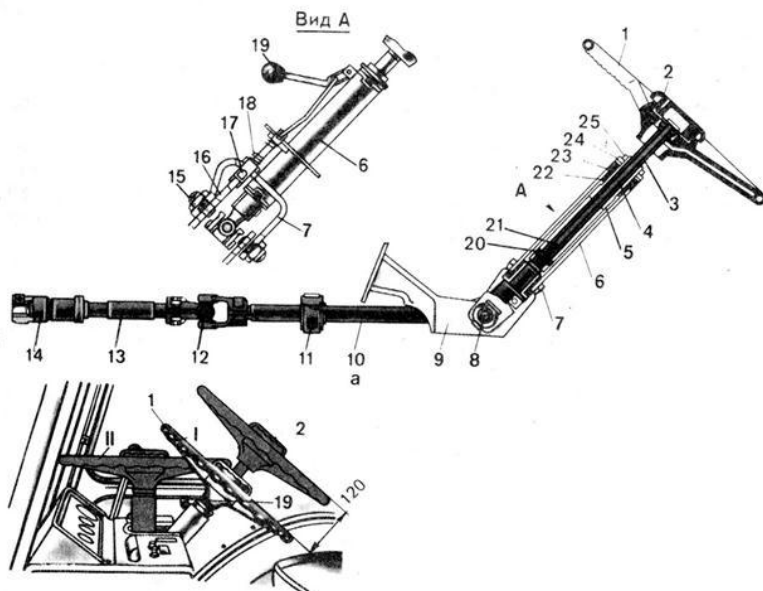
Привод рулевого механизма трактора МТЗ-80: А – конструкция привода: 1 – рулевое колесо; 2 – маховичок; 3 – рулевой вал; 4 и 15 – винты; 5 – промежуточный вал; 6 – труба рулевой колонки; 7 – серьга; 8 и 12 – карданные шарниры; 9 – стойка; 10 – средний вал; 11 – промежуточная опора; 13 – передний вал; 14 – шлицевая втулка; 16 – правая стенка стойки; 17 – фиксатор; 18 – пружина; 19 – рукоятка; 20 и 24 – гайка; 21 – штифт; 22 – втулка; 23 – амортизатор; 25 – контрагайка; б – различные положения рулевого колеса; I и II – положения рулевой колонки.
